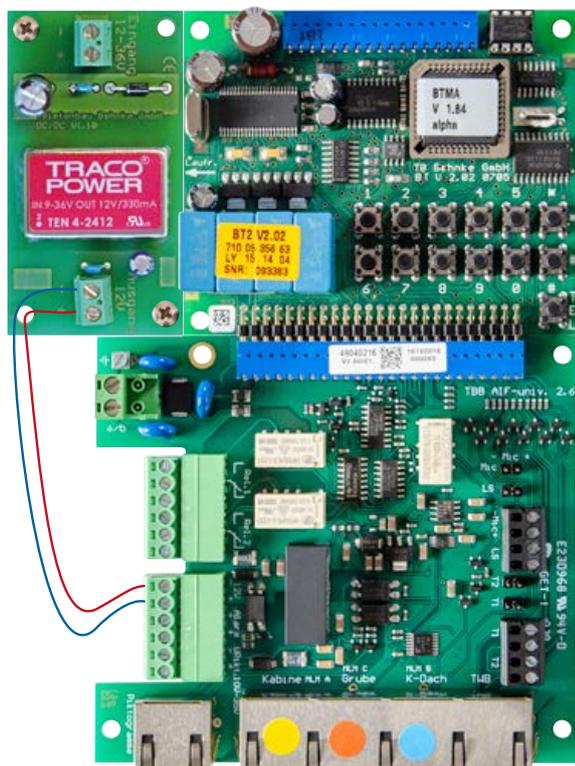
Universalgerät mit eingebautem DC / DC-Wandler
